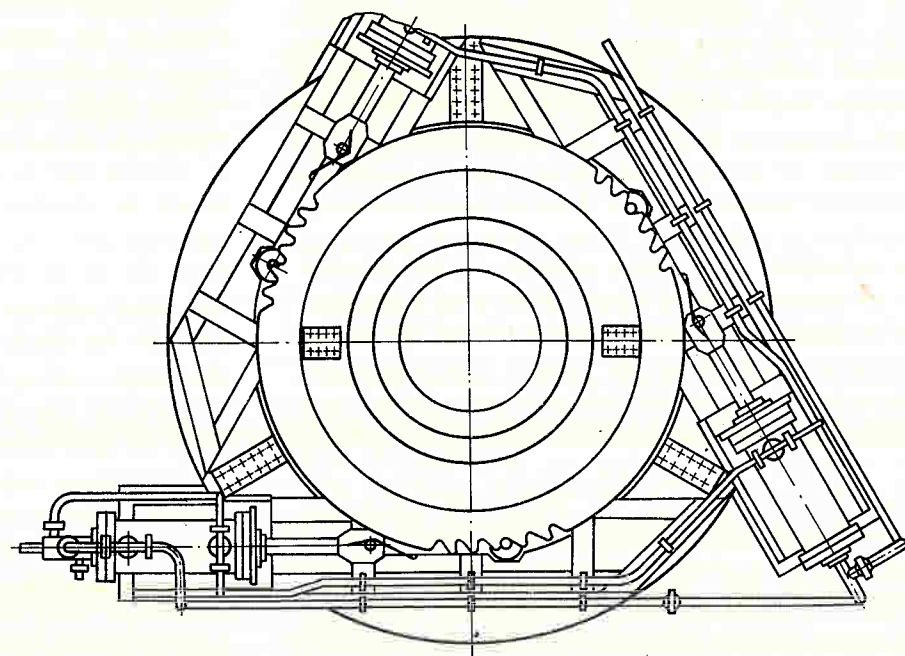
Устройство для поворота ротора гидроагрегата (с тремя сервомоторами)
